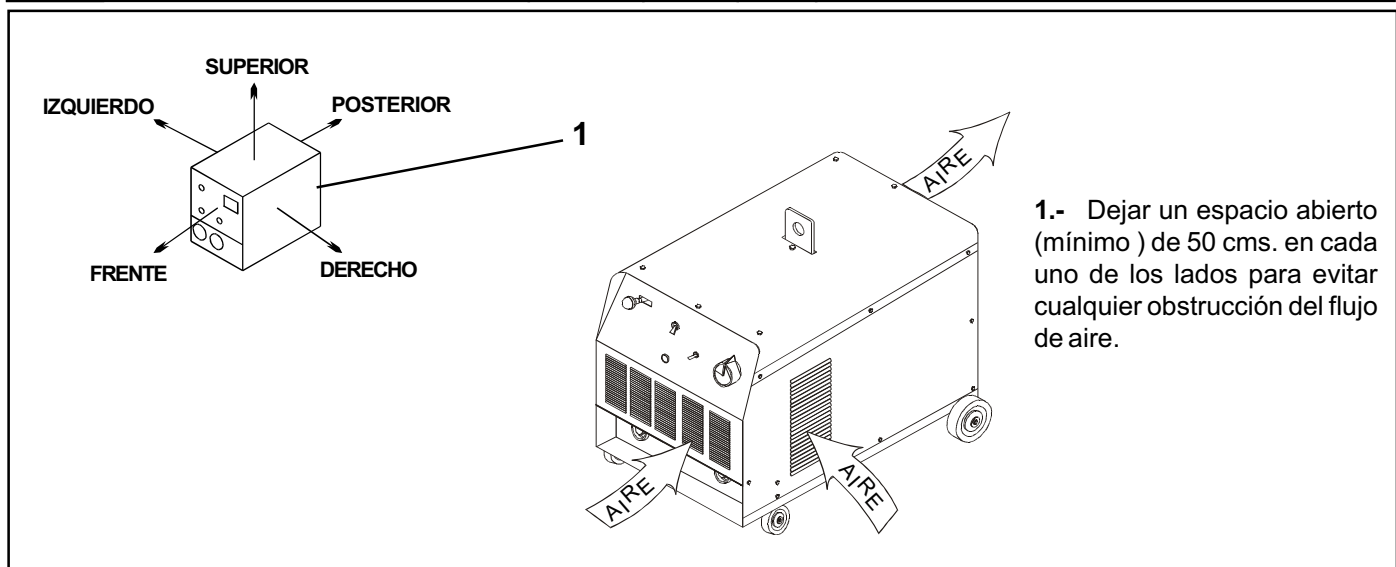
LOCALIZACION Y MOVIMIENTO DE LA MAQUINA SOLDADORA
